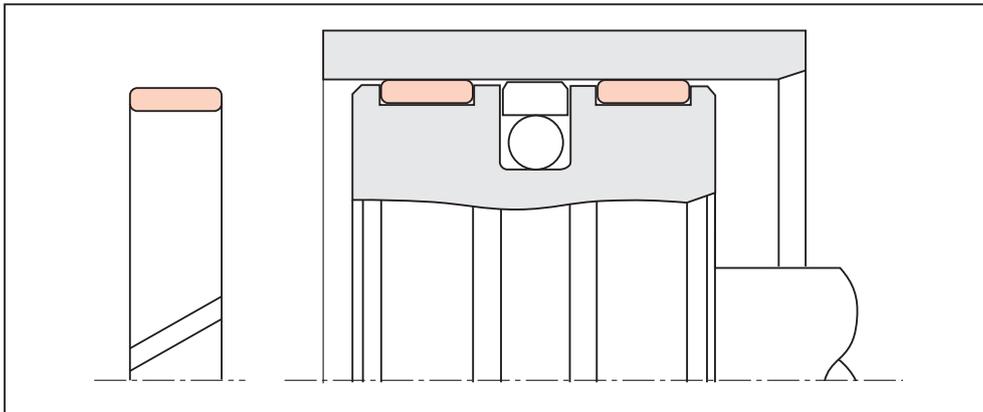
Sistema di guida pistone standard / Standard wear rings application on piston
